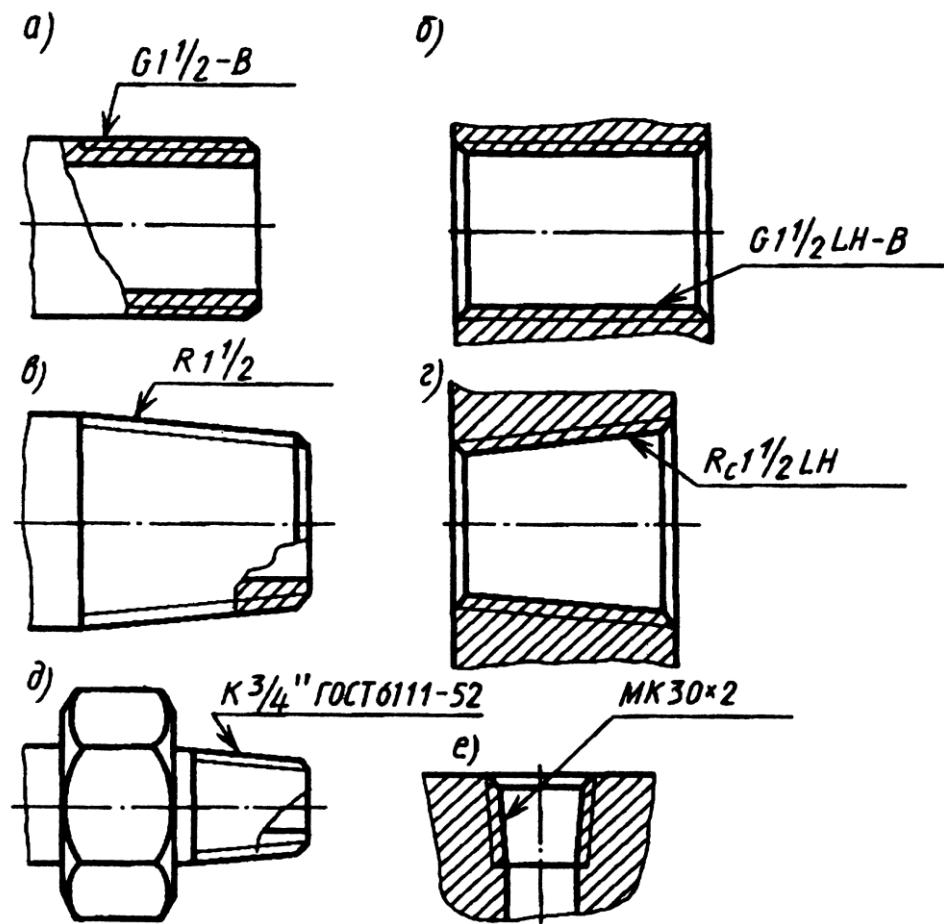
Условные обозначения трубной и конической резьб: в мм; а – трубная цилиндрическая резьба  $1\frac{1}{2}$ " класса точности B – резьба того же размера и класса точности левая; б – наружная трубная коническая резьба  $1\frac{1}{2}$ "; г – внутренняя трубная коническая резьба  $1\frac{1}{2}$ "; д – коническая дюймовая размера  $\frac{3}{4}$ " (с углом профиля  $60^\circ$ ); е – метрическая коническая диаметром 30 мм и шагом 2 мм.
